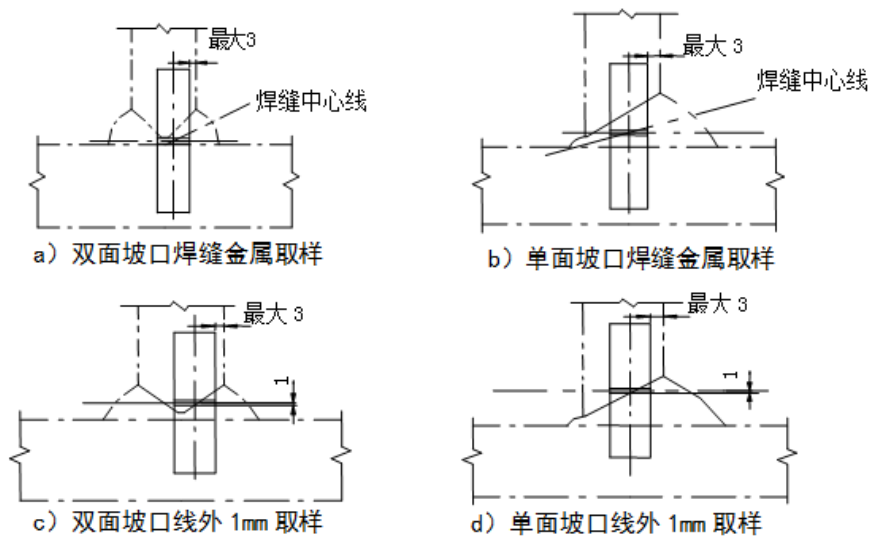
熔透角焊缝的冲击试样取样
